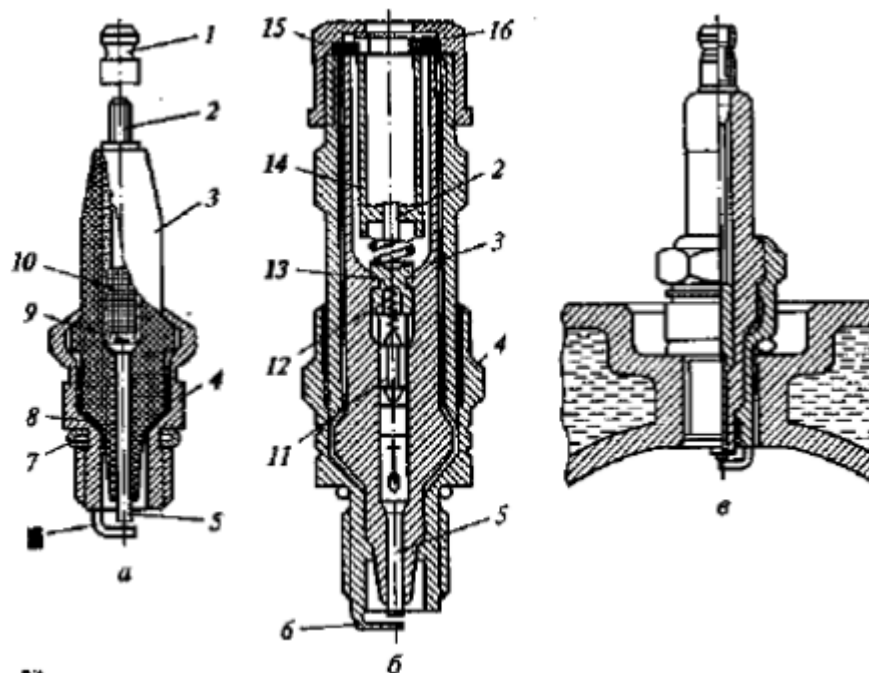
Свечи зажигания: стандартная (а), экранированная (б) и установка свечи в головке блока цилиндров двигателя (в): 1 – колпачок; 2 – стержень; 3 – изолятор; 4 – корпус; 5 и 6 – центральный и боковой электроды; 7 – уплотнительная шайба; 8 – уплотнитель; 9 – токопроводящий стеклогерметик; 10 – накатка в нижней части стержня; 11 – резистор; 12 – пружина; 13 – проводник; 14 – керамическая втулка; 15 – гайка; 16 – резиновая втулка
